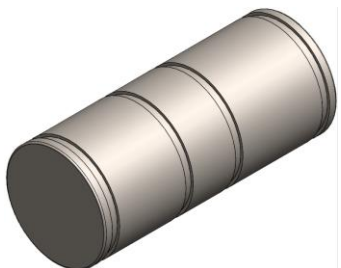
Modelo geométrico CAD 3D del eje del engrane planeta.
